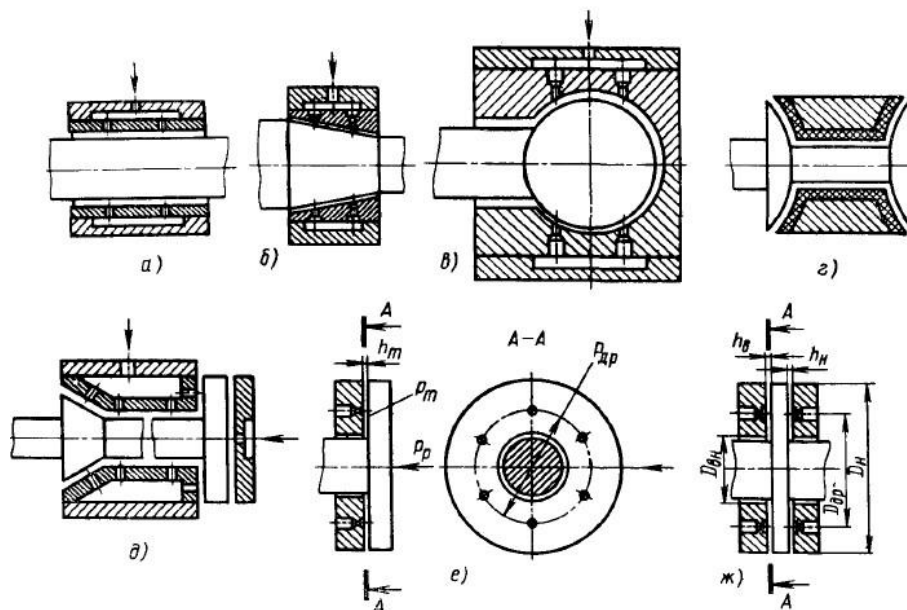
Газостатические подшипники ШУ пассивного типа: а – цилиндрический; б – конический; в – сферический; г – полусферический двусторонний; д – комбинированный; е, ж – упорный.
